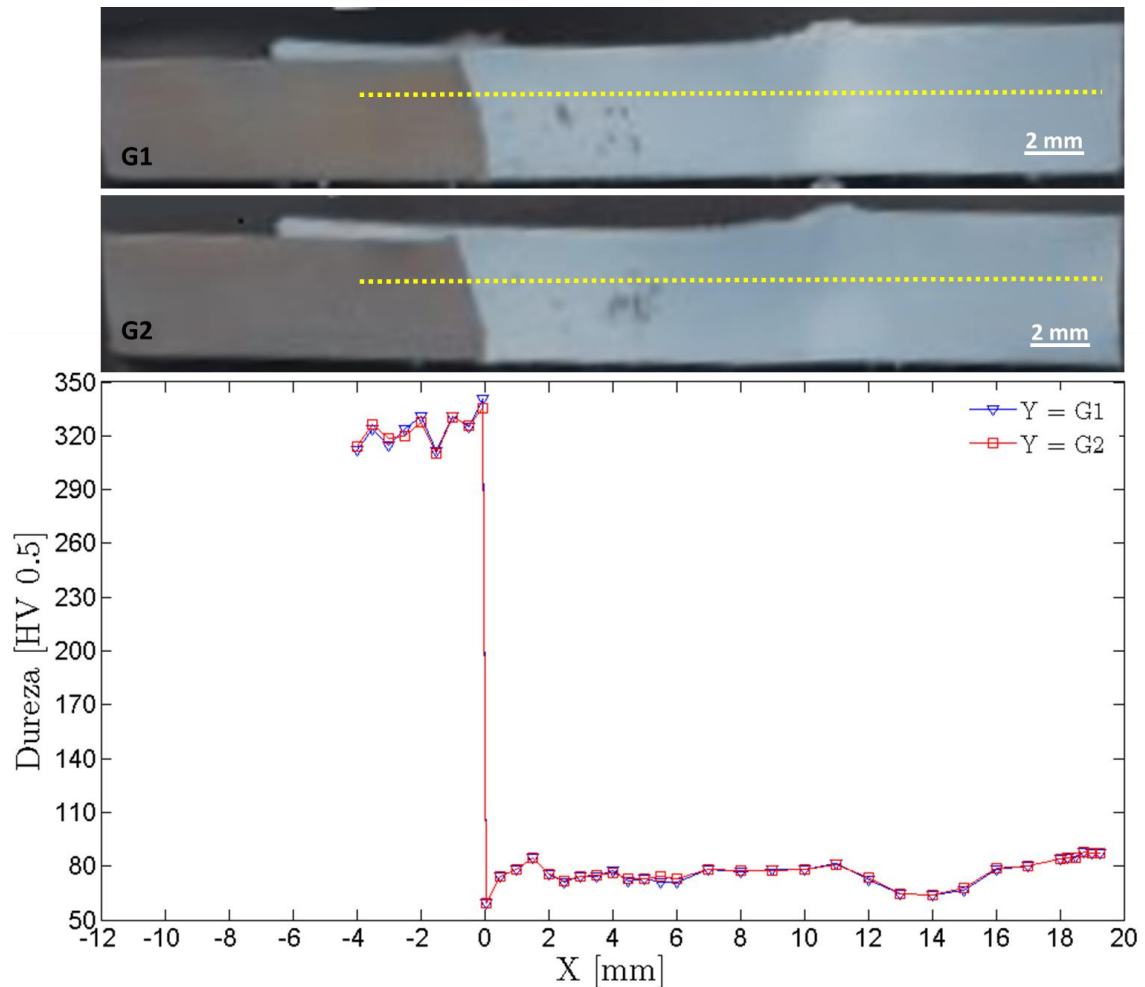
Sobreposição dos perfis de dureza do cordão de soldadura da amostra G1 e G2, $y = 2.5$ mm da base.
